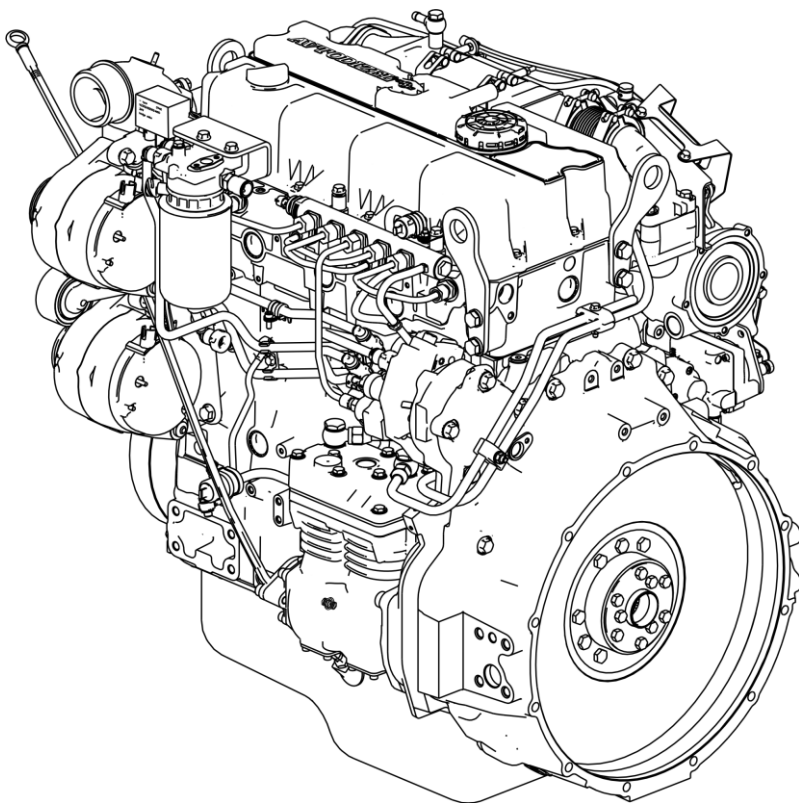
а – Двигатель ЯМЗ-53403 (общий вид слева)
